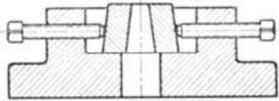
Froschplatte für auswechselbare Schnittplatten.
